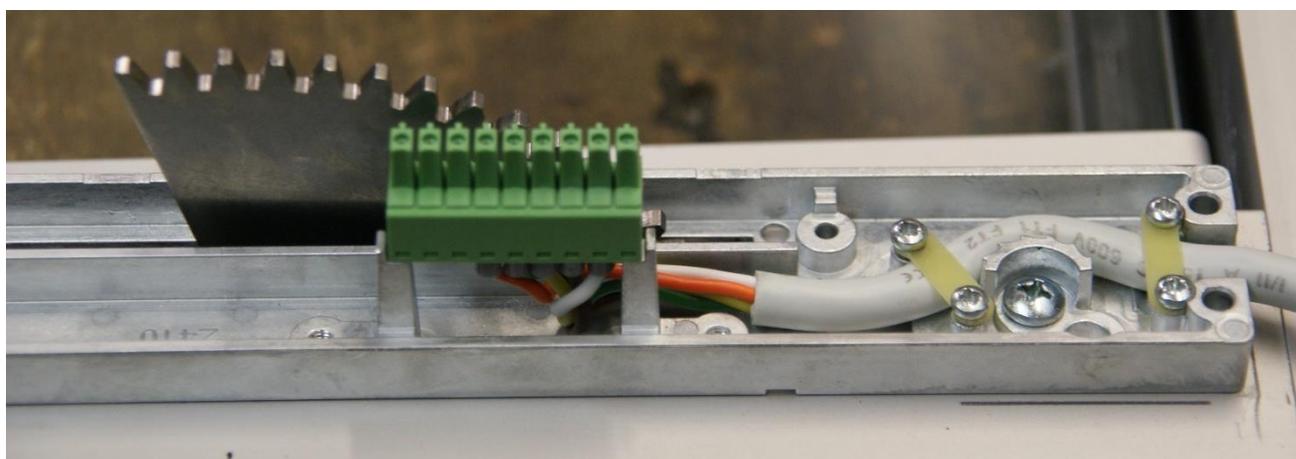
LAH 65 24 V mit der Kabelführung von oben
